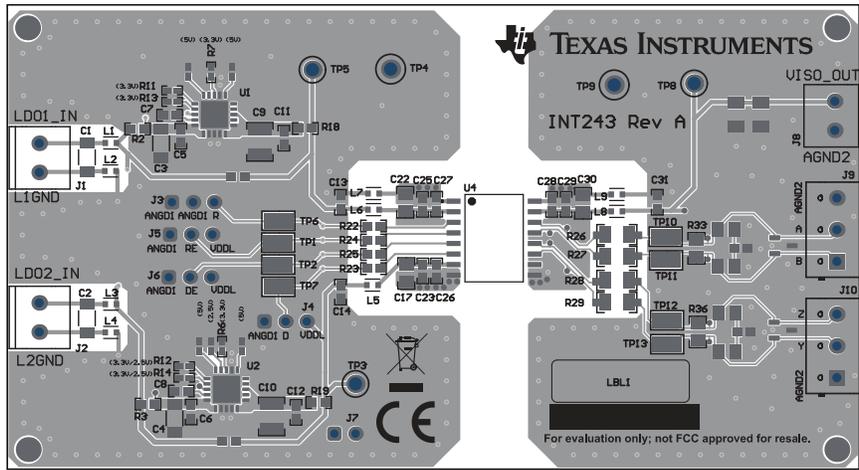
ISOW3080DWEEVM PCB 布局 - 顶层
